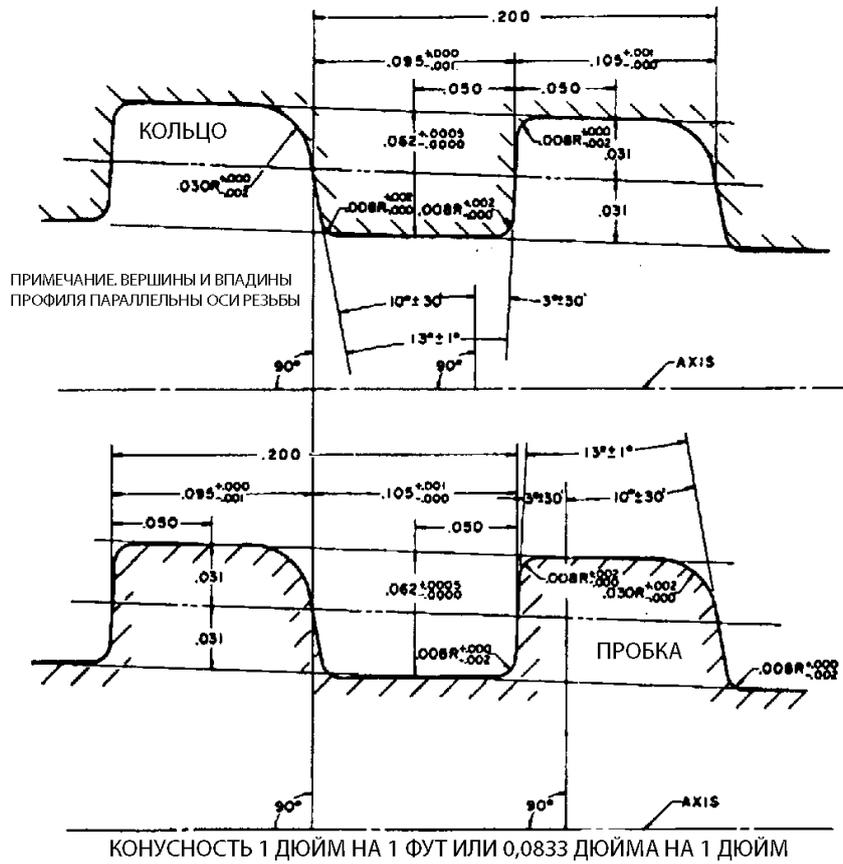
Резьбовой калибр для резьбы батресс на обсадных трубах
